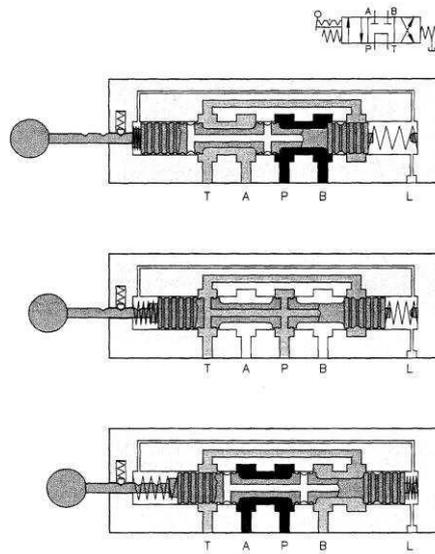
Katup 4/2.penggerak tombol , pembalik pegas (4/2 DCV push-button actuated, spring centered)
